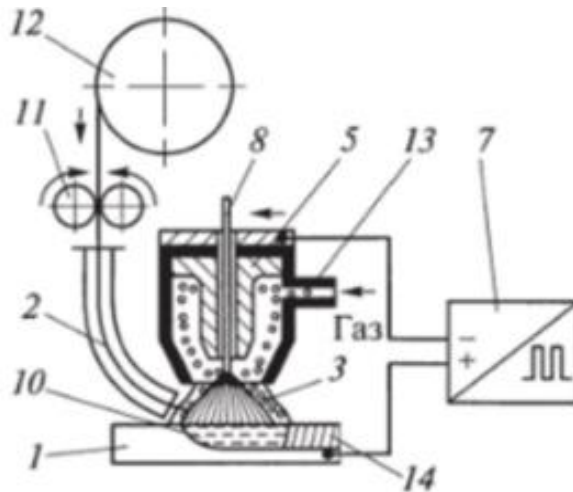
Схема зварювання в захисних газах: 1 – заготовка; 2 – присадковий пруток (дріт); 3 – дуга; 4 – корпус; 5 – мундштук; 6 – рукоятка; 7 – джерело живлення; 8 – електрод; 9 – захисний газ; 10 – ванна розплавленого металу; 11 – роликівий механізм; 12 – касета; 13 – патрубок; 14 – зварений шов
